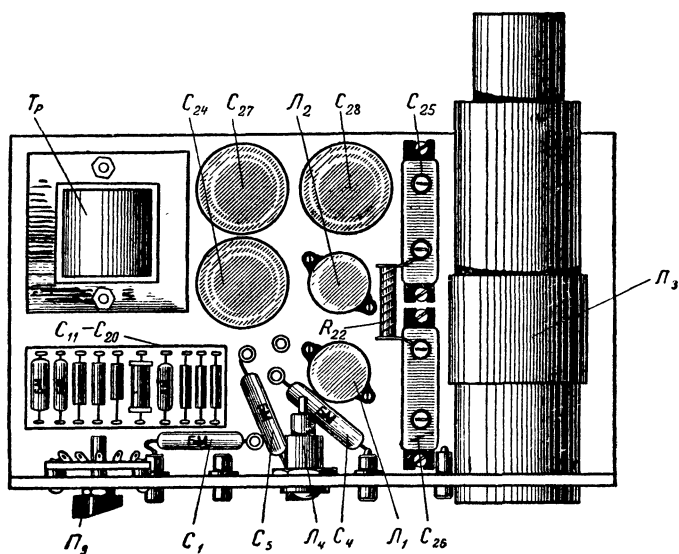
Расположение деталей на шасси прибора (вид сверху).
